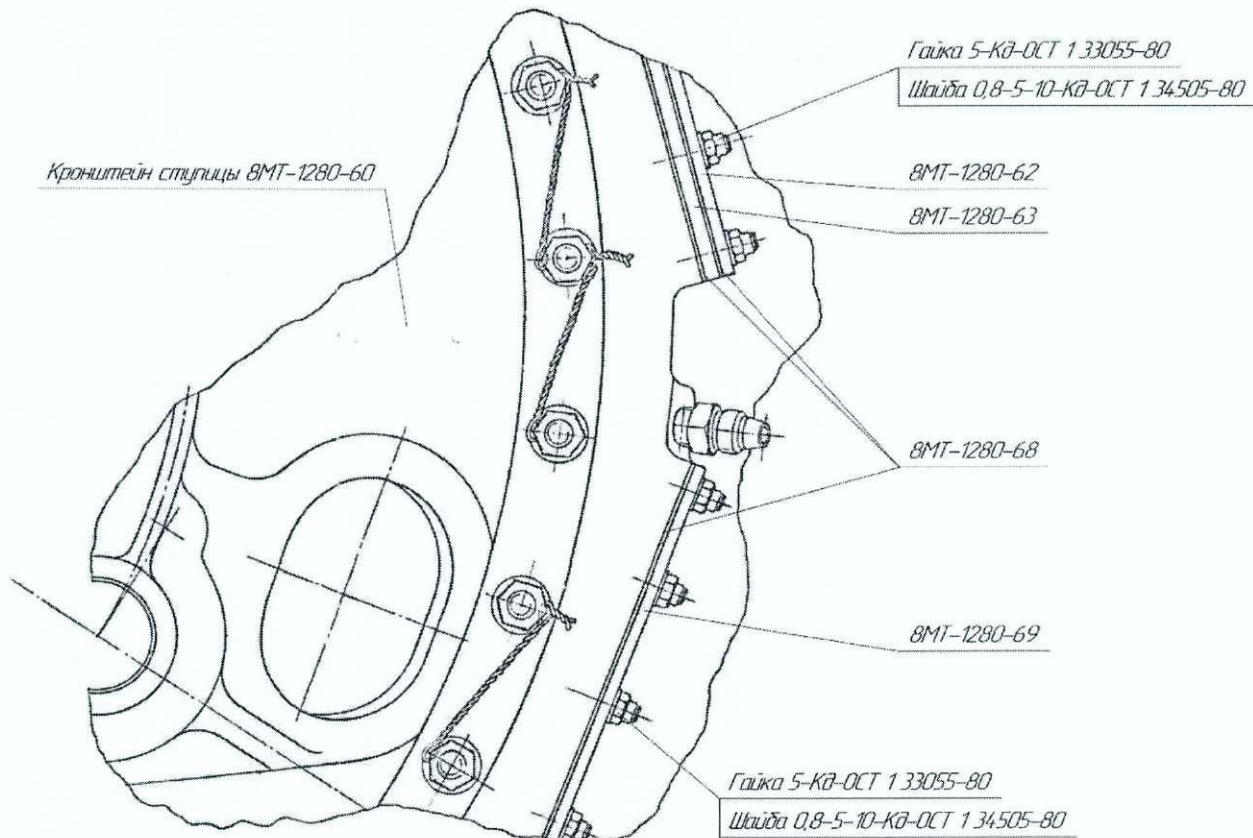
Эскиз установки прокладок 8МТ-1280-68
